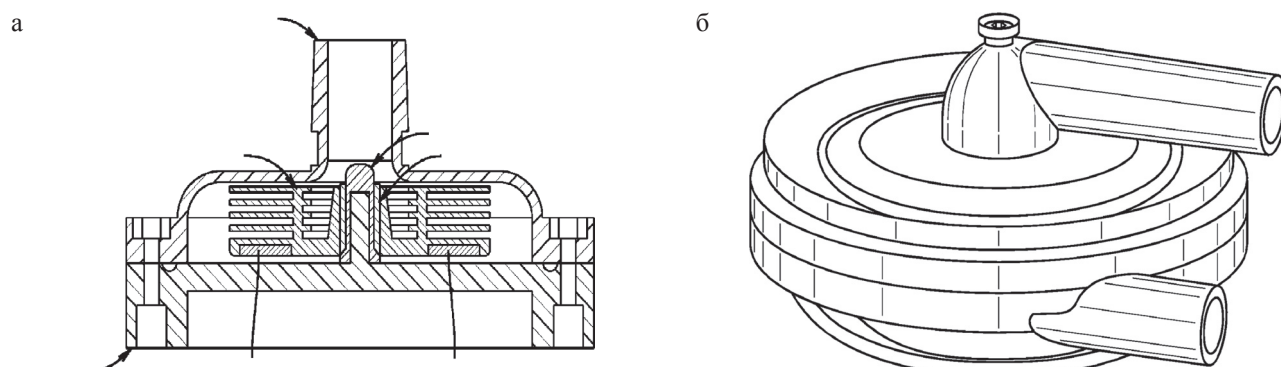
Варианты конструкции корпуса насосов Тесла для перекачивания крови [10]: а – корпус насоса с вертикальным расположением приточного патрубка; б – корпус насоса с горизонтальным расположением приточного патрубка
